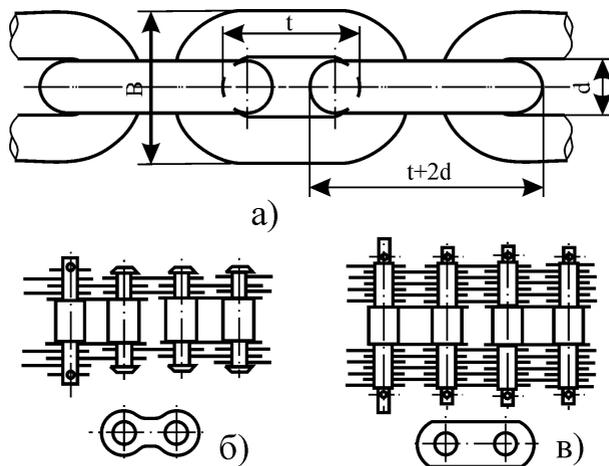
Цепи: а — сварная; б, в — пластинчатые
